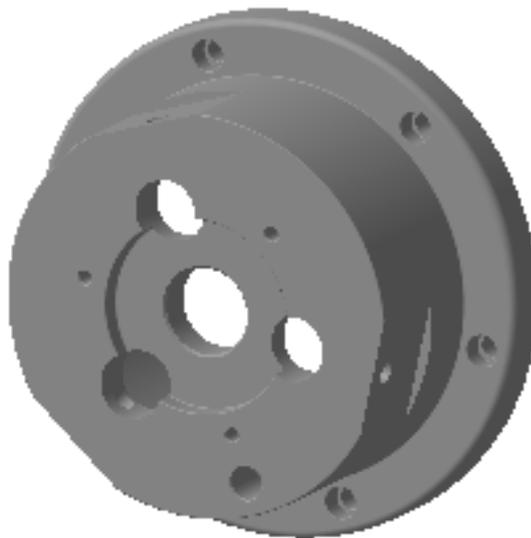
Трех мерный вид корпуса наладочного приспособления
